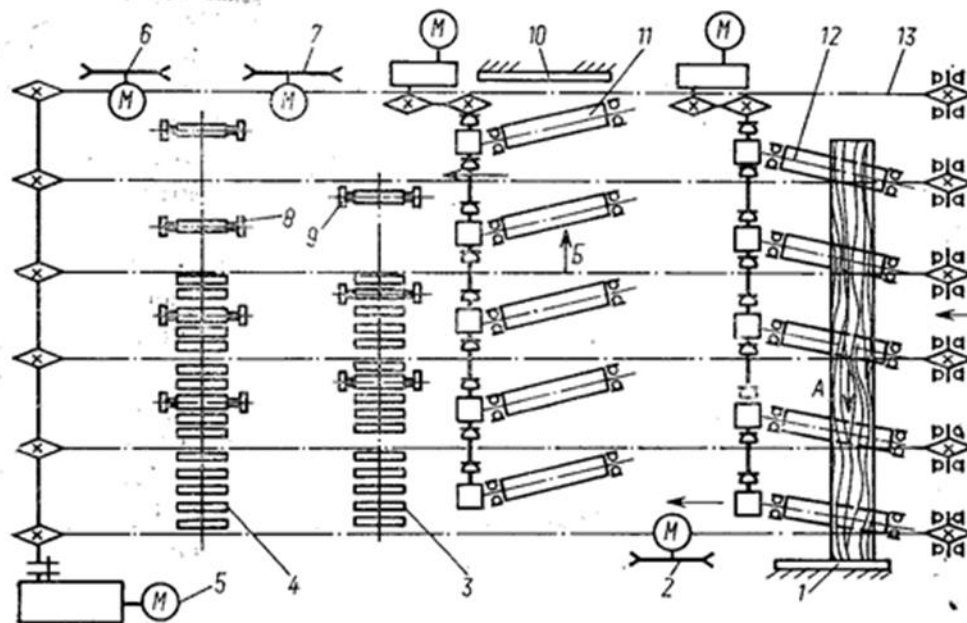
Схема трехпильной торцовочной установки ЦЗТ-2М
